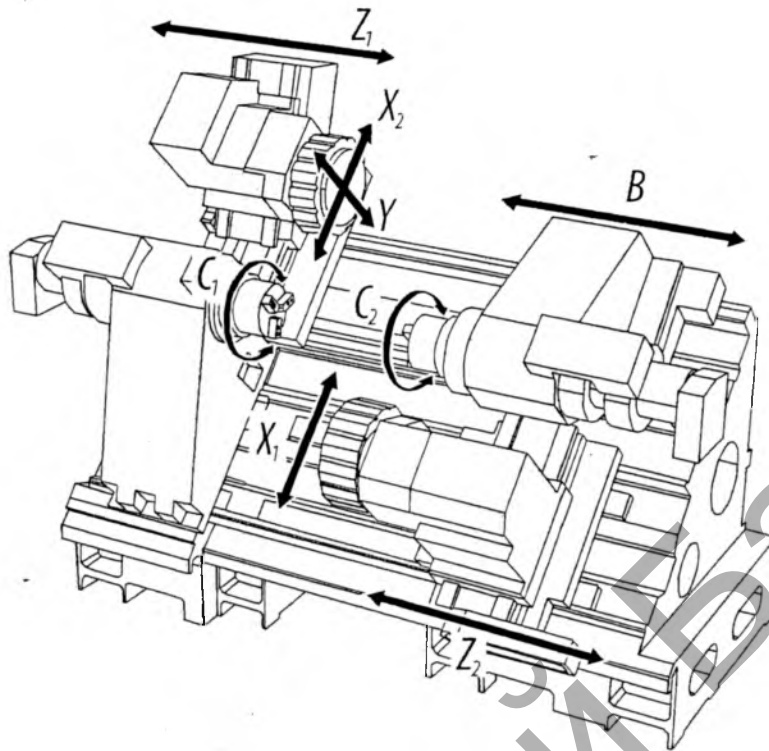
Положение осей у токарного станка с ЧПУ с контршпинделем и двумя револьверными головками
